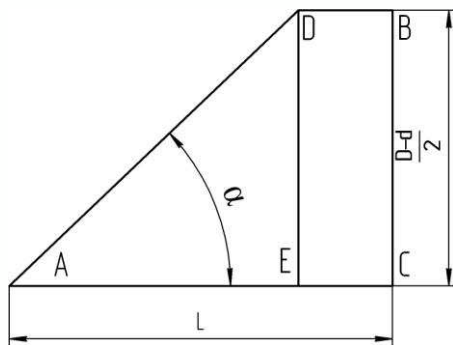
Розгортка фрезоведучої поверхні руйнівного елемента
